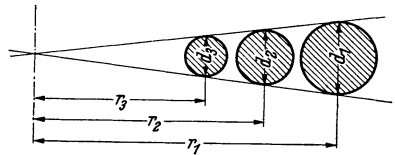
Zur Berechnung der Schraubenfedersätze.
